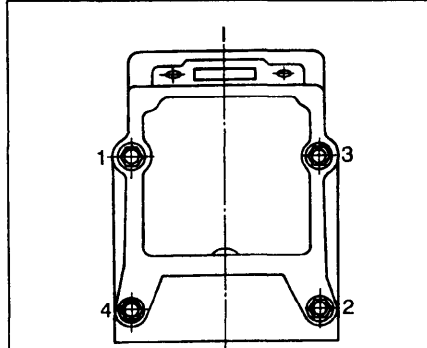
Порядок затяжки болтов крепления головки цилиндров
